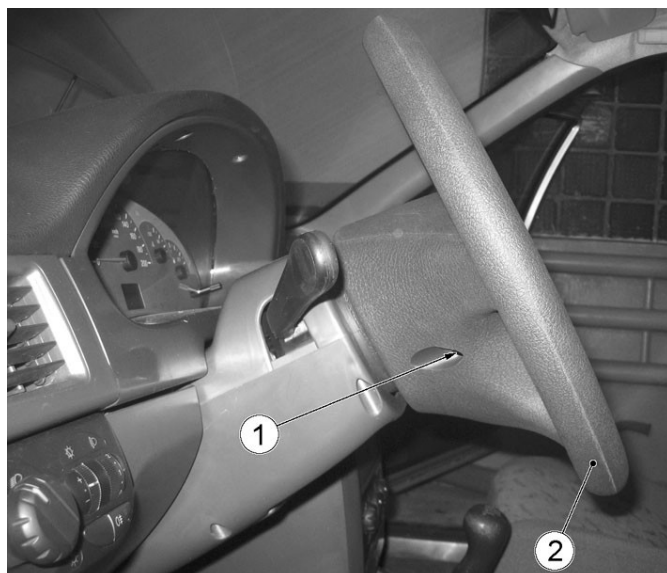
Расположение болтов крепления модуля газогенераторного:
